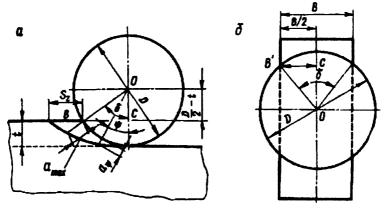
Схема резания при цилиндрическом (а) и торцевом (б) фрезеровании
